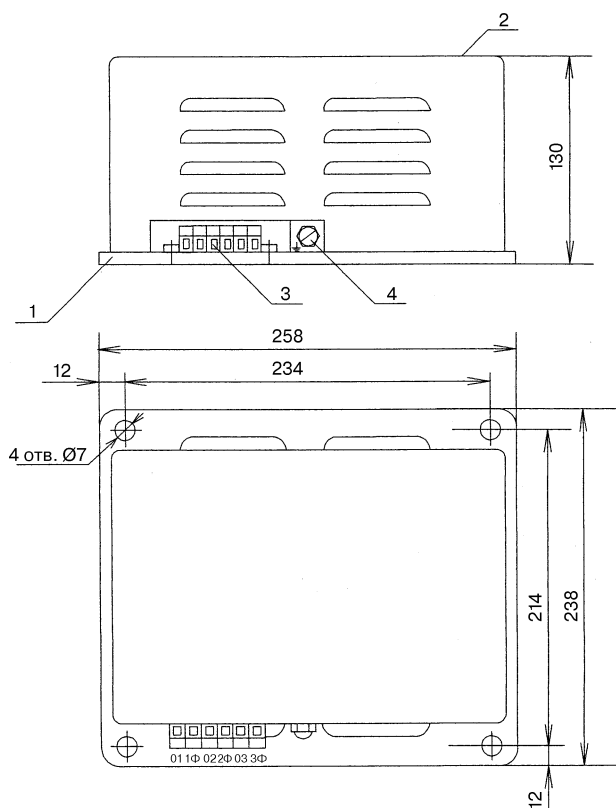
Внешний вид блока БЗПЗ-25 и БЗПЗ-100, где: 1 — основание; 2 — кожух; 3 — клемменный соединитель; 4 — винт заземления
